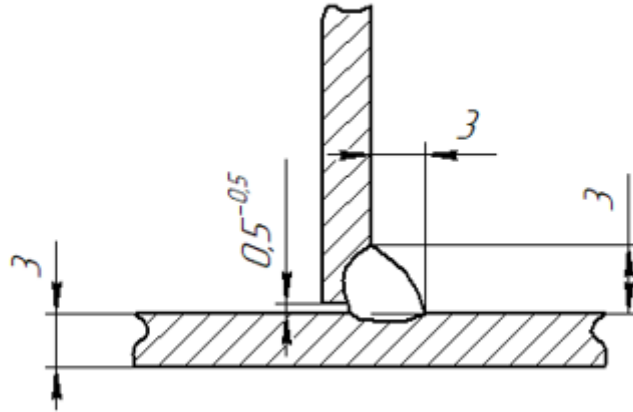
Тип зварних з'єднань твердопаливної печі
